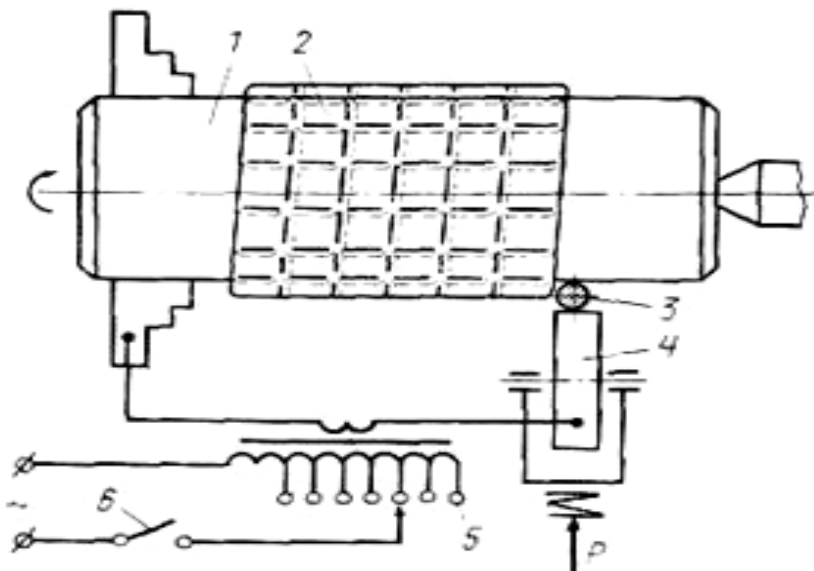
Основна технологічна схема електроконтактного наплавлення 1 — деталь, що наплавляється, 2 — наплавлений метал; 3 — присадний дріт, 4 — наплавляючий ролик; 5 — трансформатор, 6 — переривник струму
